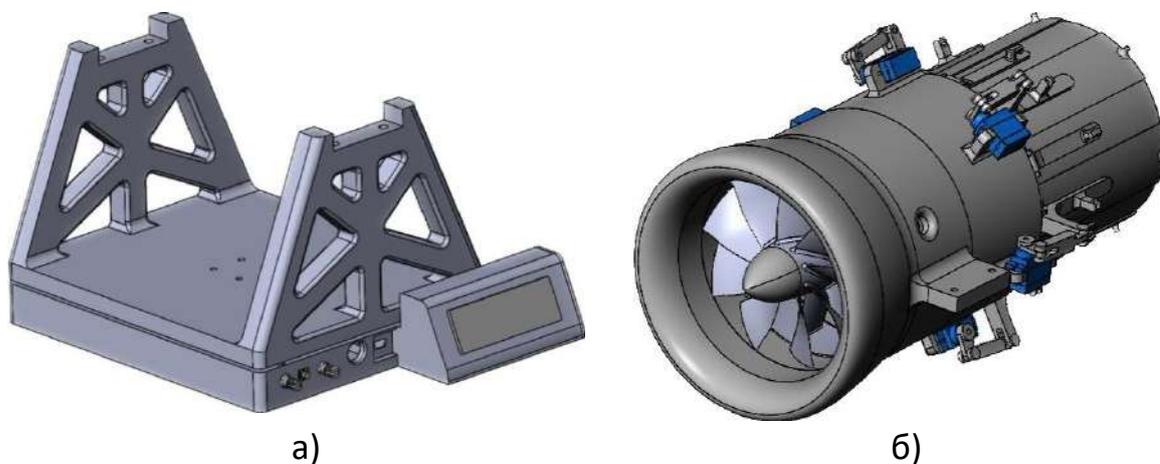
Стенд: (а) – рама стенда, (б) – вентилятор
